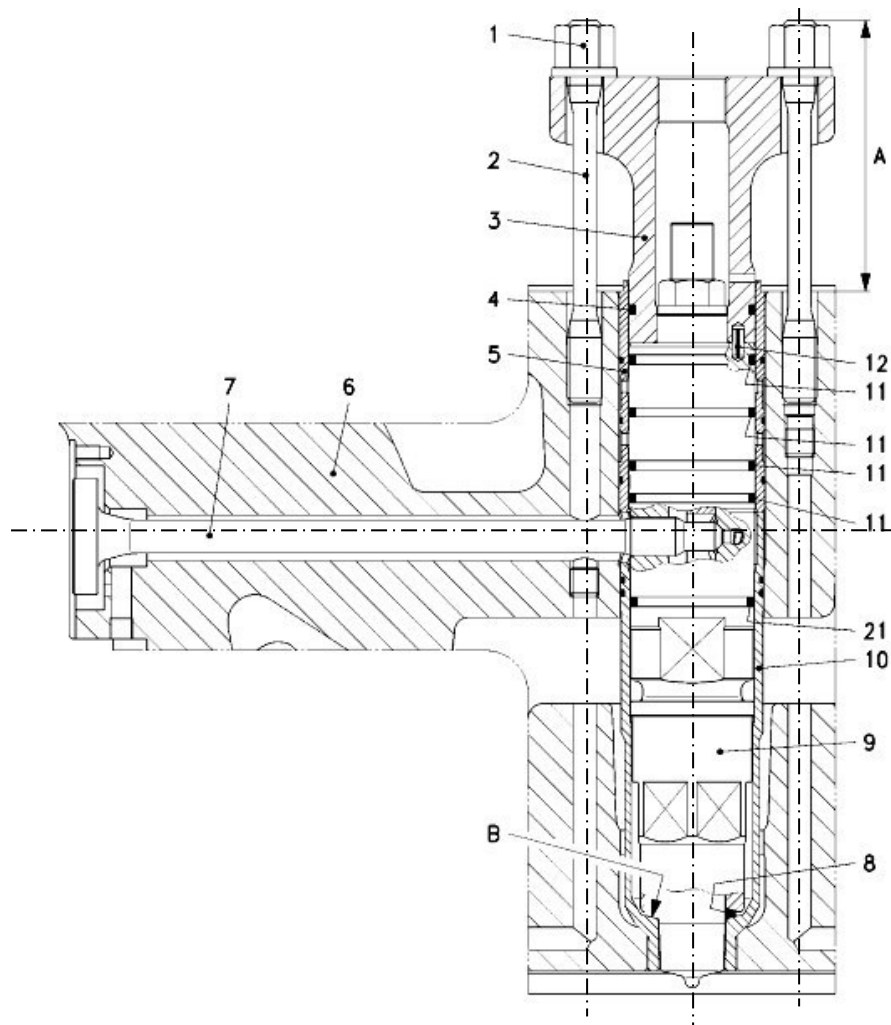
Форсунка з різьбовим з’єднанням: 1 - шестигранна гайка; 2 – стойка; 3 - упорний фланець; 4, 11, 21 - О-подібне кільце ущільнення; 5 – втулка; 6 - головка циліндра; 7 - різьбовий елемент; 8 - ущільнююче кільце; 9 - форсунка; 10 – вставка; 12 – штифт; А – болтова відстань; В – сідло клапана
